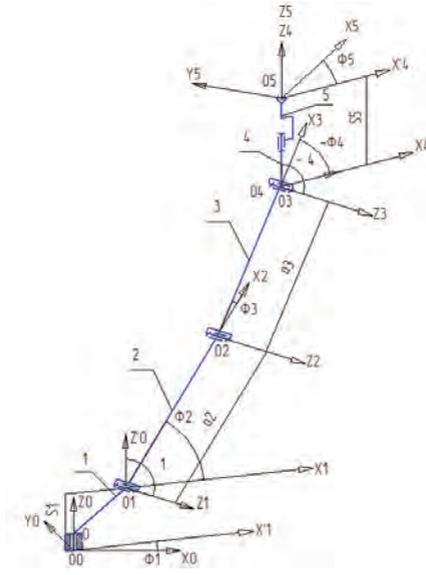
Кинематическая схема манипулятора робота KUKA Robotics KR 30 L16 - 2 с нанесенными началами координат для каждой кинематической пары и для каждого звена
